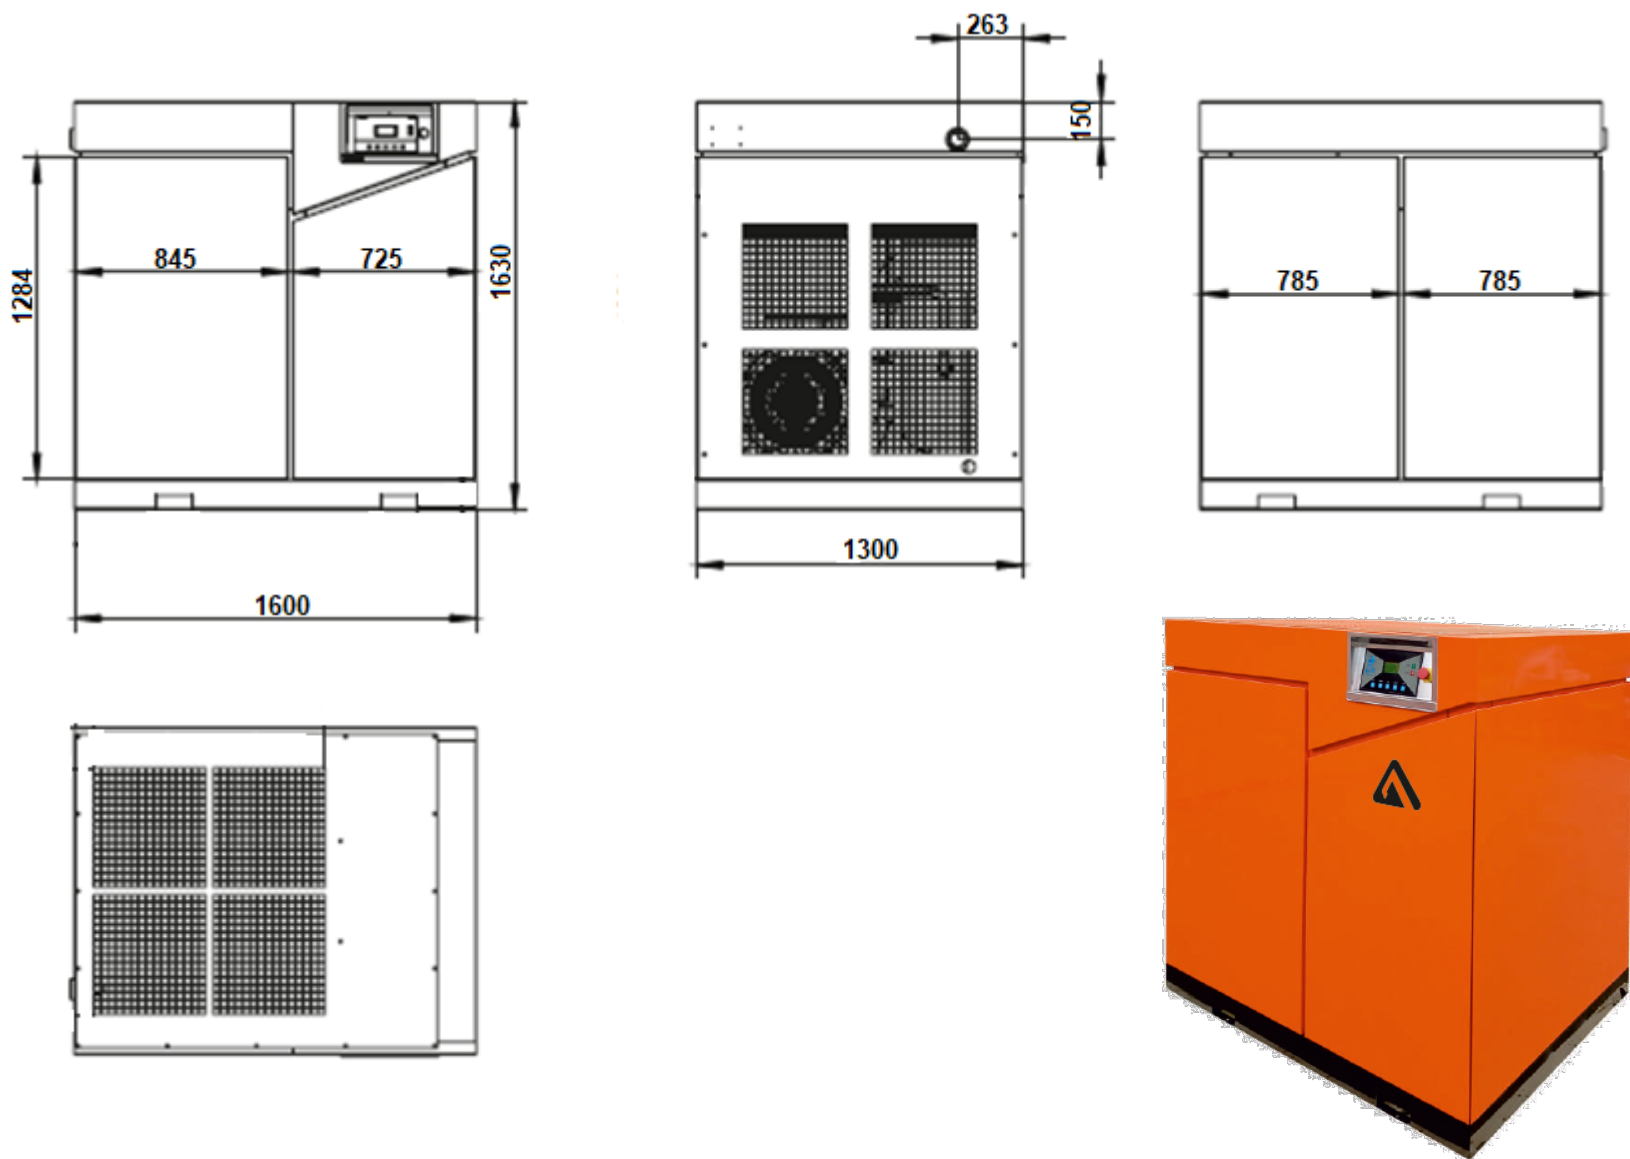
Общий вид, габаритные размеры станции компрессорной ЗИФ-СВЭ типа АРМ с двигателем 75 кВт
